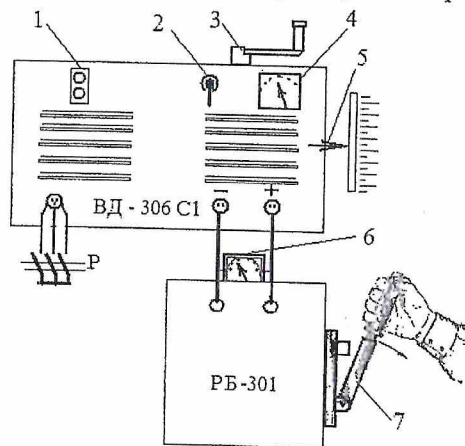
Схема опытной установки для определения внешней характеристики выпрямителя: 1-выключатель с кнопками «пуск» и «стоп»; 2 - переключатель ступеней тока; 3-рукоятка регулятора сварочного тока; 4 - амперметр; 5- указатель сварочного тока со шкалой; 6 - вольтметр; 7-контактный нож РБ-301
